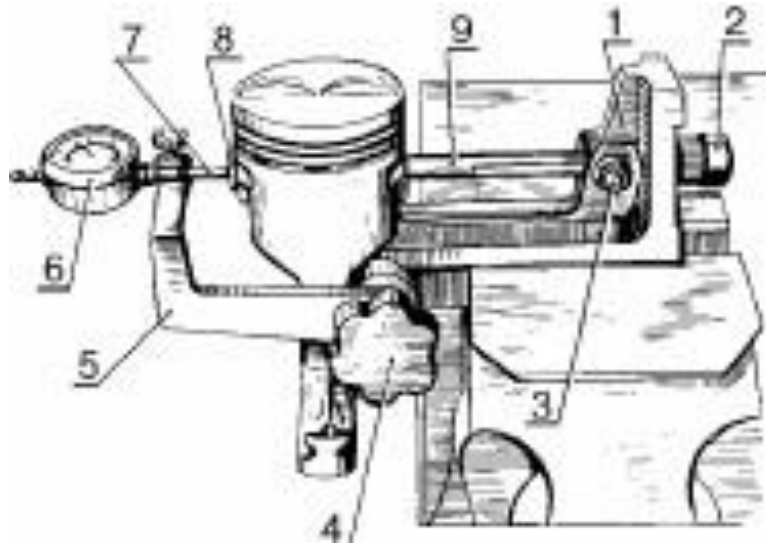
Схема перевірки запресування пальця в шатун.
